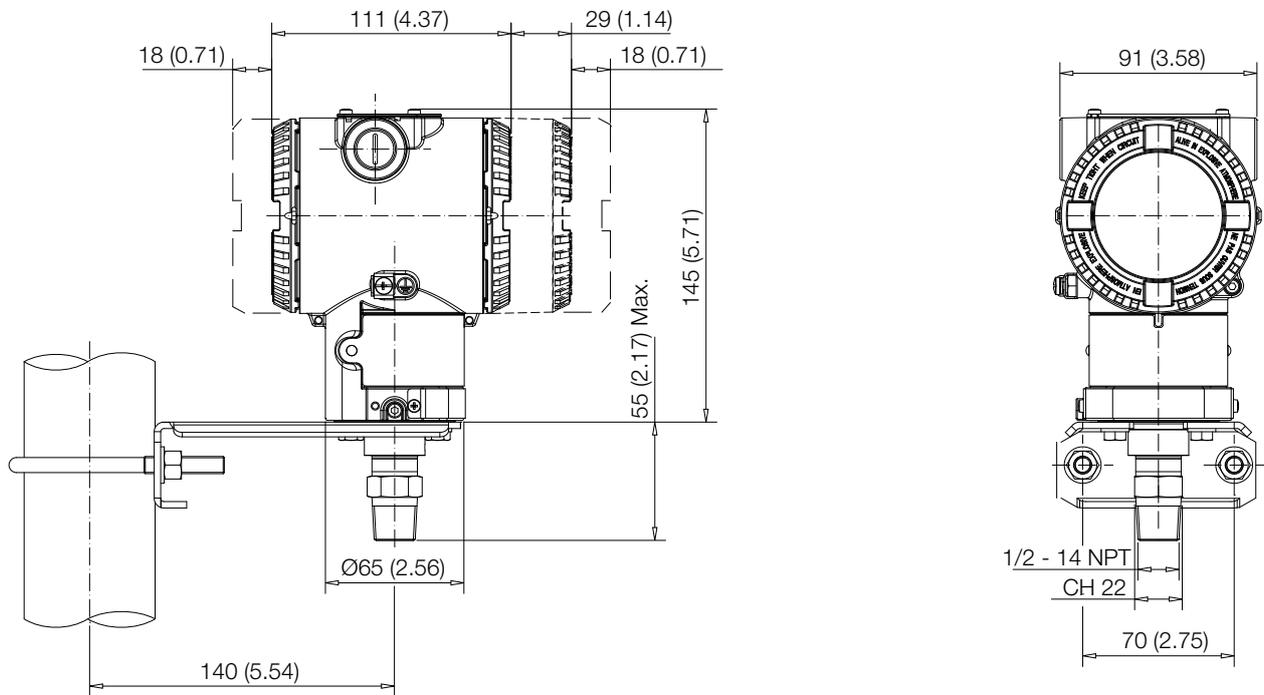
Modèle de transmetteur 266G ou 266A de type P équipé d'un boîtier de type barillet installé sur un tuyau de 2" avec support de montage en option (B1 en acier au carbone ou B2 en acier inoxydable 316L)
